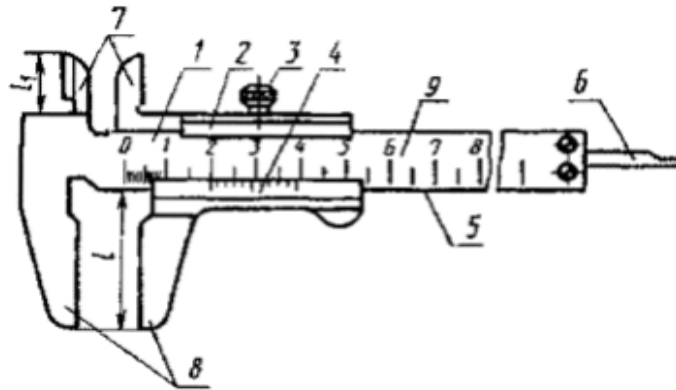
Штангенциркуль ШЦ-І 0-125
